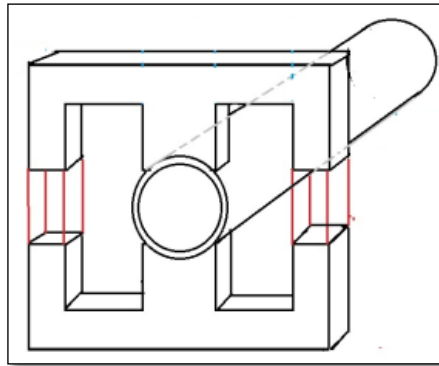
Bosquejo prototipo de la herramienta, Fuente: Autor.
